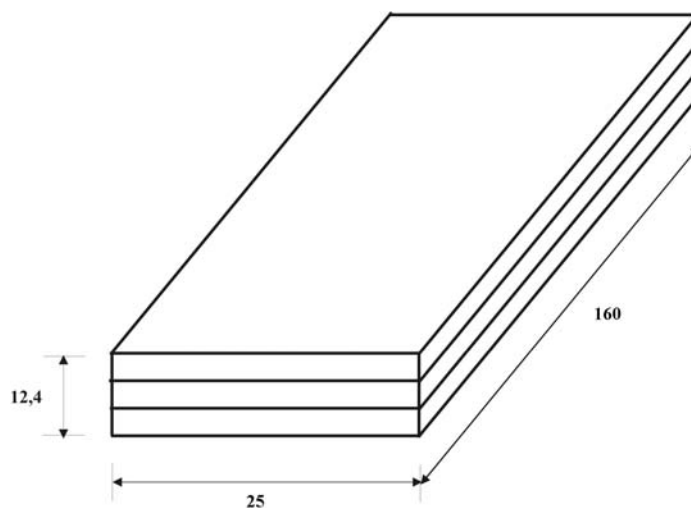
Dimensões, em mm, do corpo de prova de flexão
